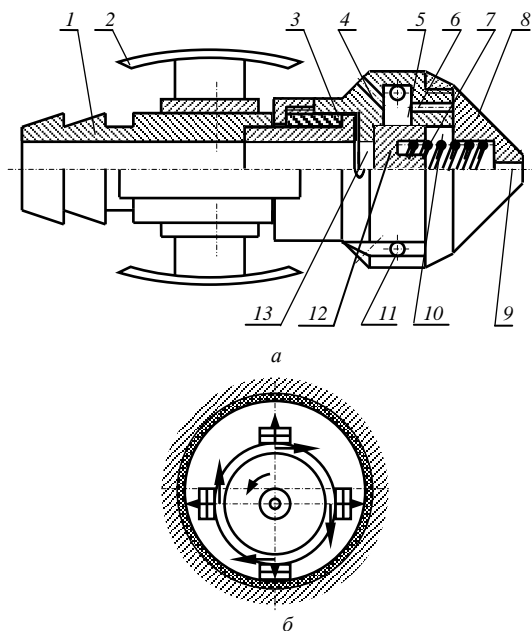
Головка с импульсной подачей воды: *а* – вид сбоку; *б* – расположение головки в дрене; 1 – штуцер корпуса; 2 – направляющие лыжи; 3 – подшипник скольжения; 4 – выходные задние отверстия; 5, 10, 13 – камеры; 6 – продольные каналы; 7 – пружина; 8 – вращающаяся головка; 9 – переднее отверстие; 11 – тангенциальные отверстия; 12 – поршень
